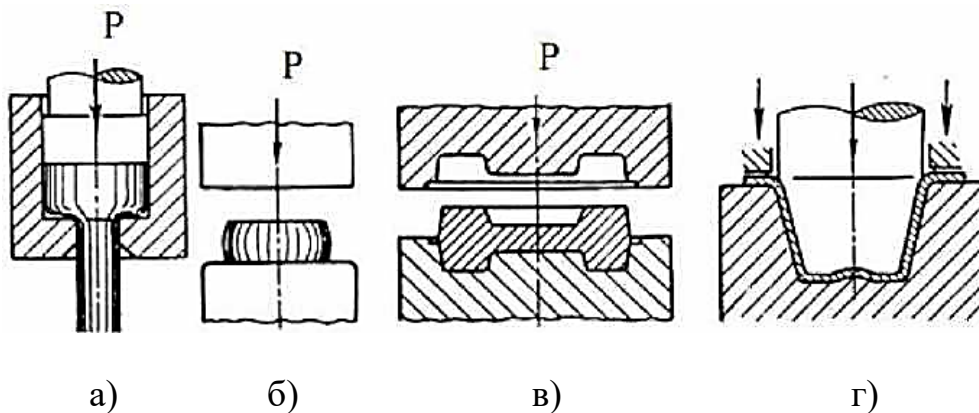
Способи отримання заготовок обробкою тиском:
